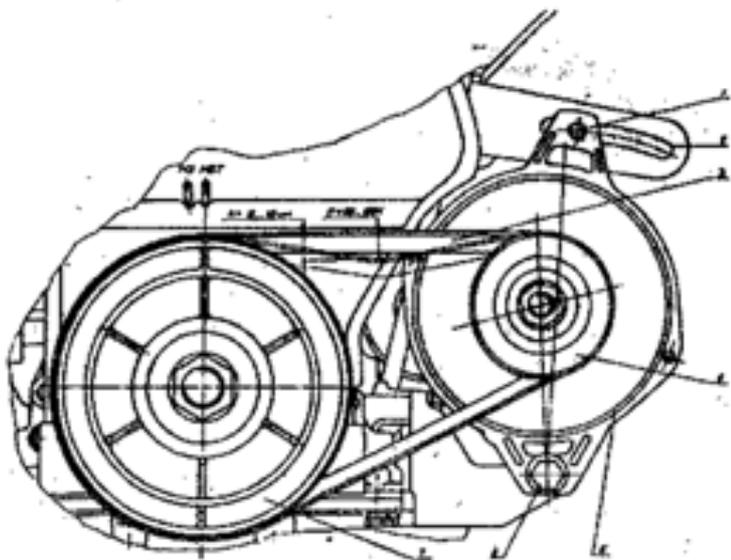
Привод генератора и проверка натяжения ремня: 1 - болт крепления генератора к натяжной планке; 2 - натяжная планка; 3 - ремень привода генератора; 4 - шкив привода генератора; 5 - генератор; 6 - два болта крепления генератора; 7 - шкив коленчатого вала
